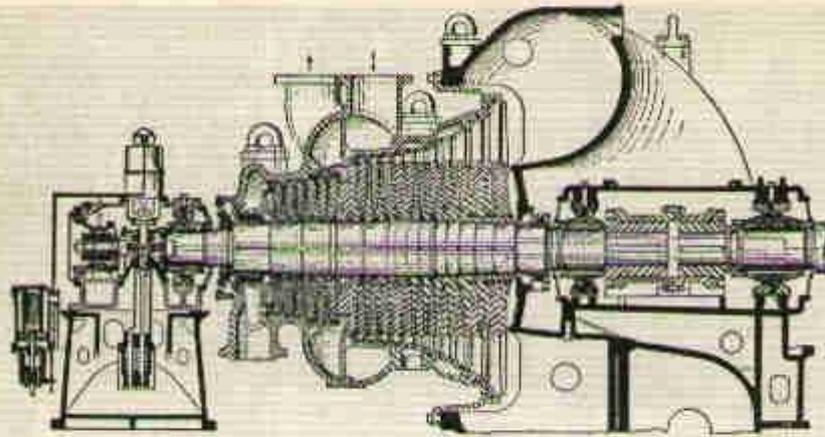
I. — Turbina de acción con recalentamiento de 19 etapas que desarrolla 35.000 kW a 1.800 v/min.
